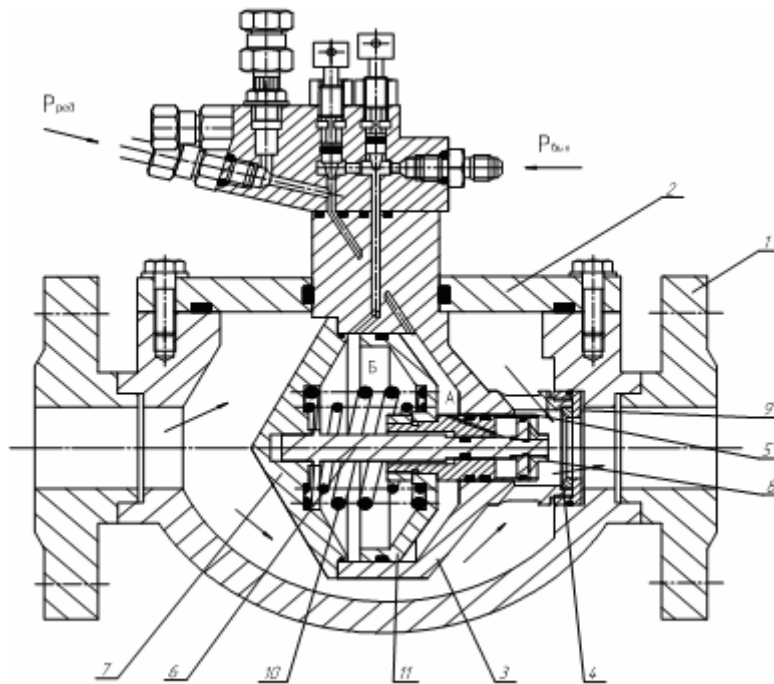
Принципиальная схема регулятора давления газа прямого действия для ГРС: 1 – корпус; 2 - вставка; 3 - гильза; 4 - седло; 5 – затвор; 6 – шток; 7 – крышка; 8 – гайка; 9 – гайка; 10 – пружина; 11 – поршень
